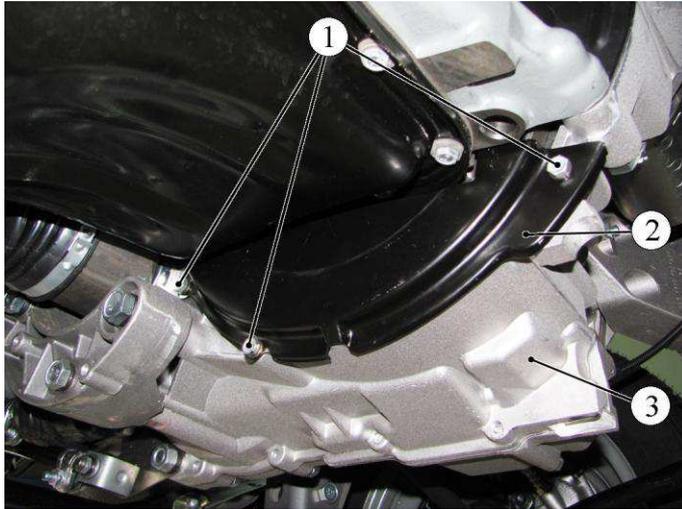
Снятие нижней крышки картера сцепления:
